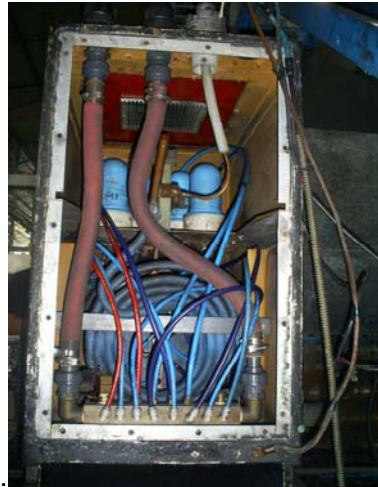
INTERIOR DEL SISTEMA DE SOLDADURA
